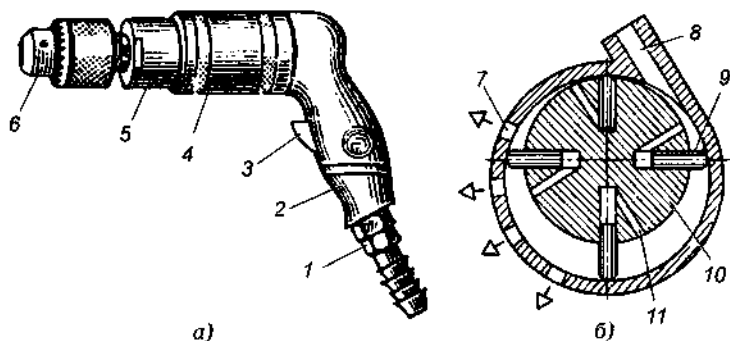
Ручная пневматическая машина: а — общий вид; б — разрез; 1 — штуцер; 2 — рукоятка; 3 — курок; 4 — корпус пневматического двигателя; 5 — корпус шпинделя; 6 — патрон; 7 — отверстие; 8 — впускное отверстие; 9 — лопатка; 10 — ротор; 11 — уравнивающее отверстие
